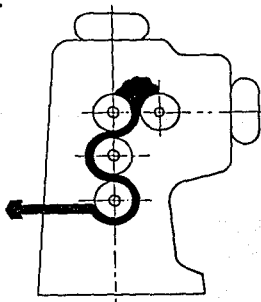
MAQUINA DE CALANDRADO.
